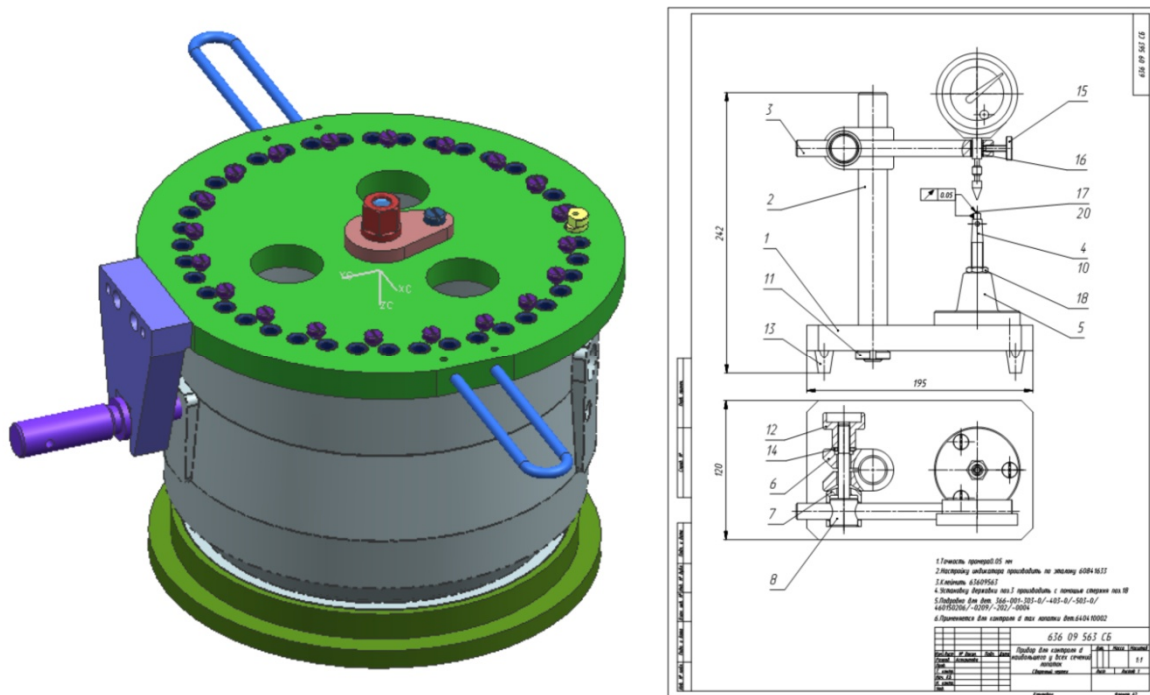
Электронная 3D-модель вновь разработанного приспособления и оцифрованный электронный сборочный чертёж существующей сборки
